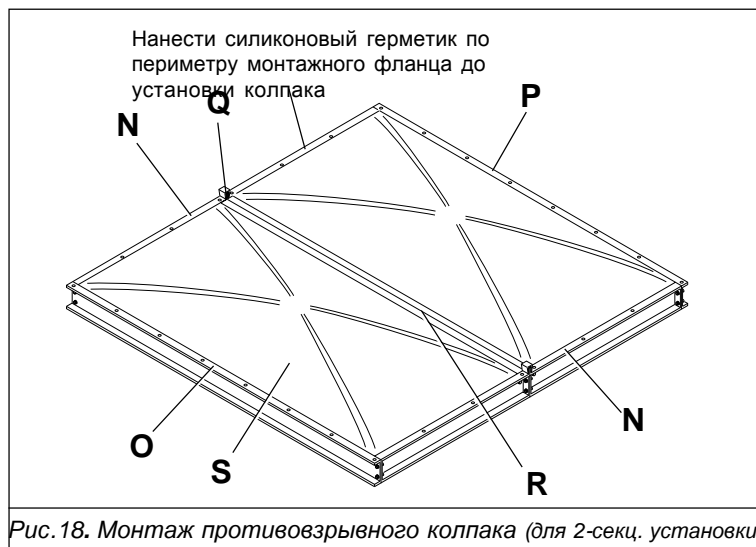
Монтаж противозрывного колпака (для 2-секц. установки)
